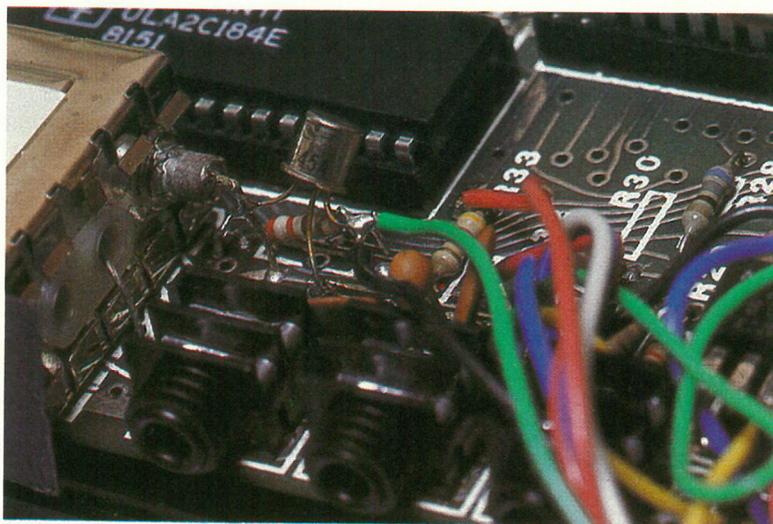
Le transistor, monté en «émetteur suiveur», est soudé à proximité du modulateur.
